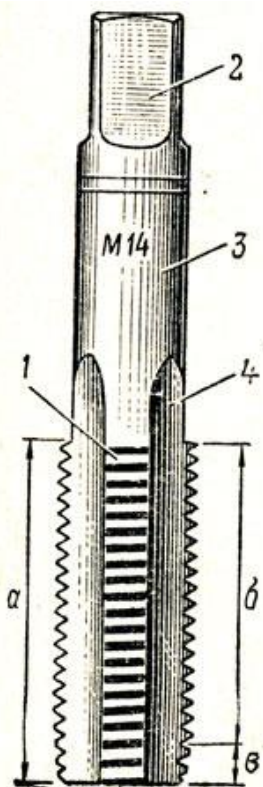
Слесарный метчик: а - рабочая часть; б - калибрующая часть; в - заборная часть; 1 - нитка (виток); 2 - квадрат; 5 - хвостовик; 4 - канавка
